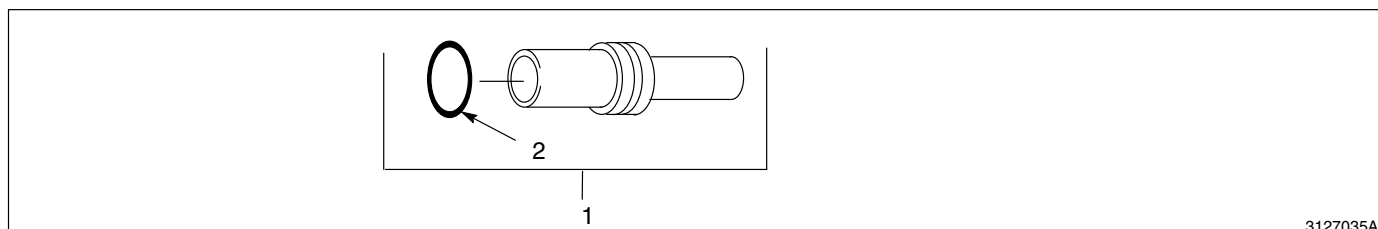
Schlauchanschlußstück für $\frac{3}{8}$ Zoll Innendurchmesser
